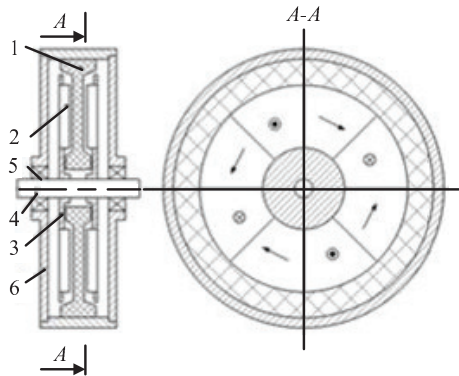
Двухсторонняя дисковая машина без магнитопроводов на статоре и роторе: 1 – обмотка беспазового безжелезного статора; 2 – ВПМ; 3 – двойной ротор; 4 – вал; 5 – подшипники; 6 – корпус
